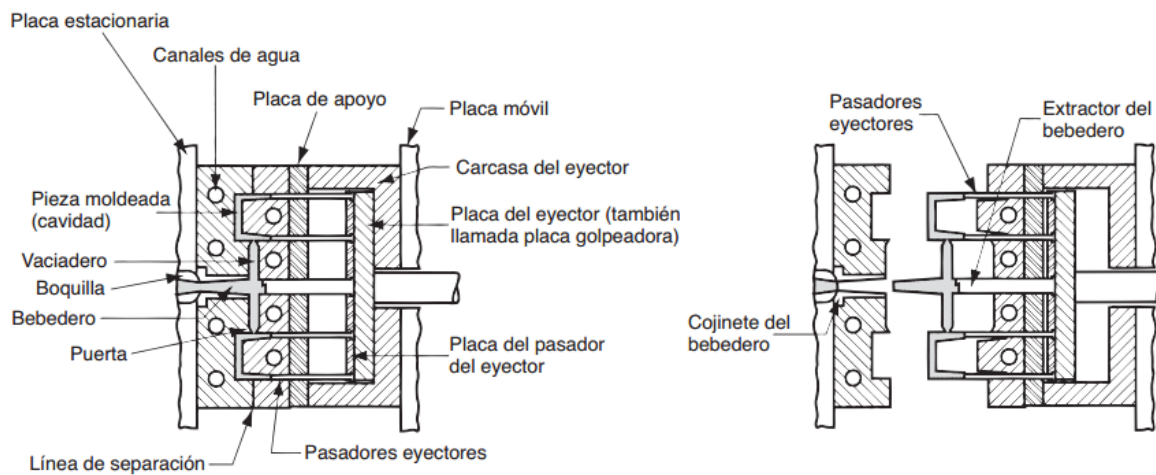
Molde de un sistema de moldeo por inyección. A la izquierda se observa un molde cerrado, mientras que a la derecha un molde abierto.
